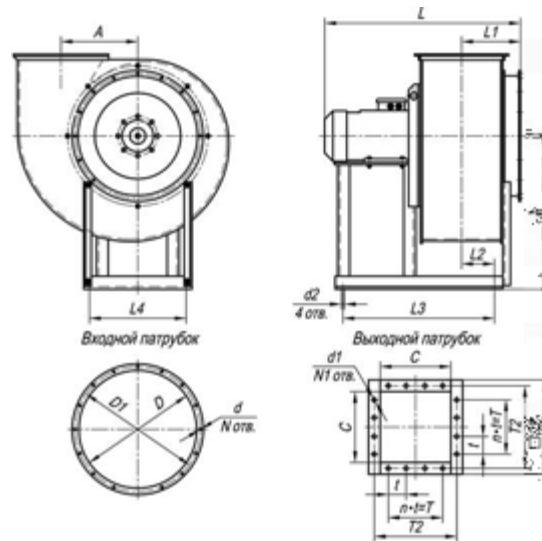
Креслення вентилятору В-Ц4-70-8
